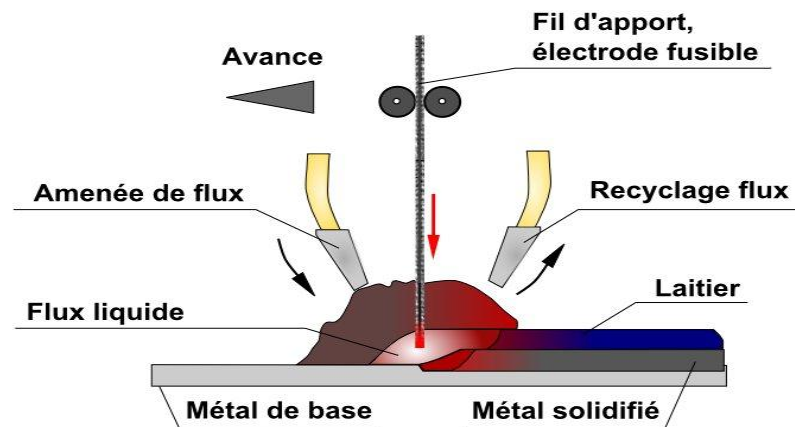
Procédé de soudage sous flux en poudre(SAW)
